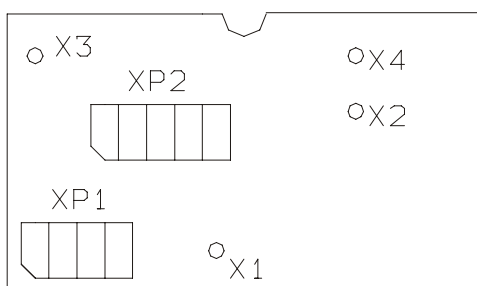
Сборочный чертеж кроссплаты блока датчика СКГГ варианта исполнения 1.
